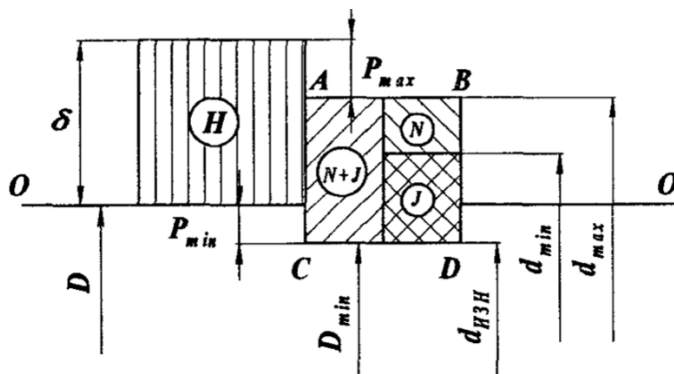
Схема розташування полів допусків під час розрахунку виконавчих розмірів розвертки:
